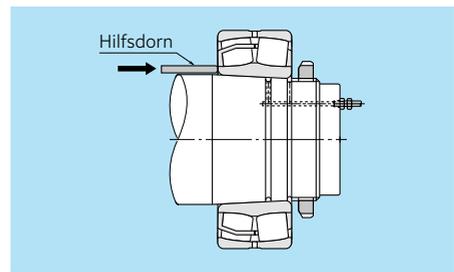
Lagerdemontage mit Ölhydraulik
